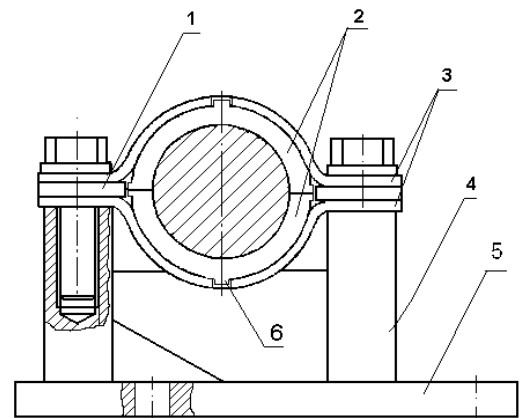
Узел трения клавишного солоотряса: 1 – металлическая прокладка; 2 – полуподшипники из композитов; 3 – металлические каркасы; 4 – металлический корпус; 5 – основа (плита); 6 – шпоночный выступ
